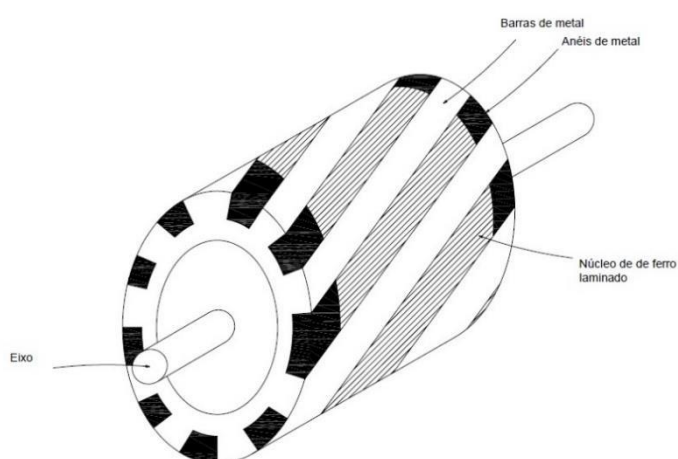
Vista do rotor de um motor de indução (Fonte do autor).
